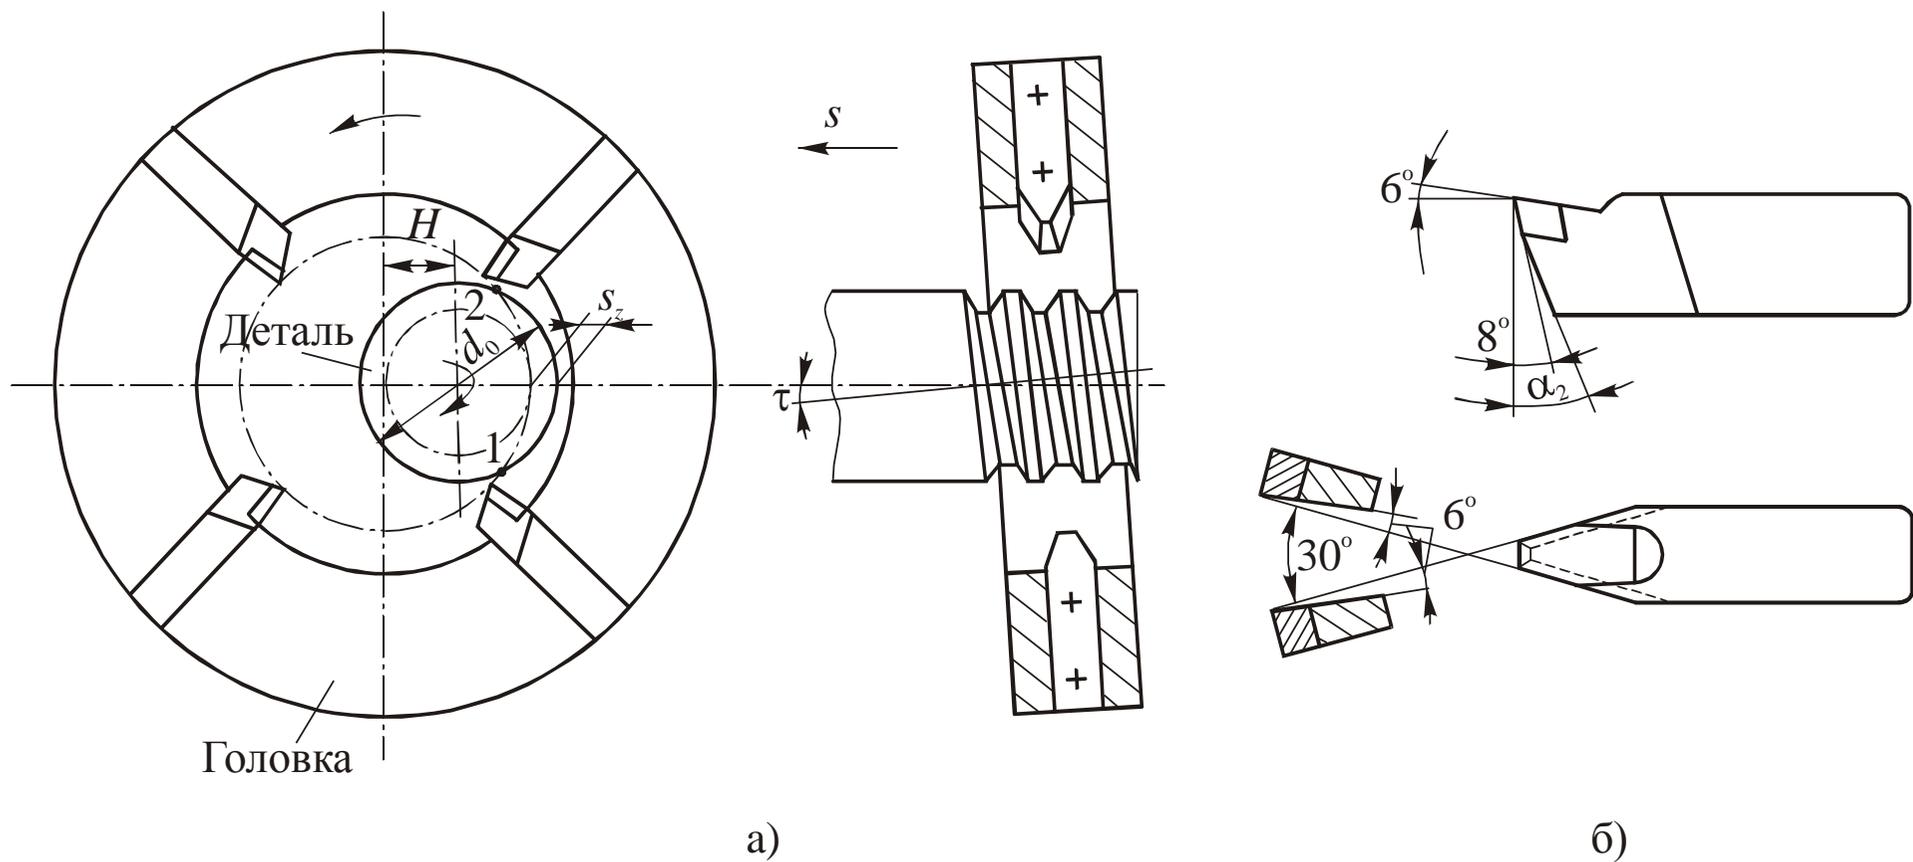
Схемы «вихревого» резьбофрезерования многорезцовыми головками: *а* – схема головки; *б* – конструкция резца
